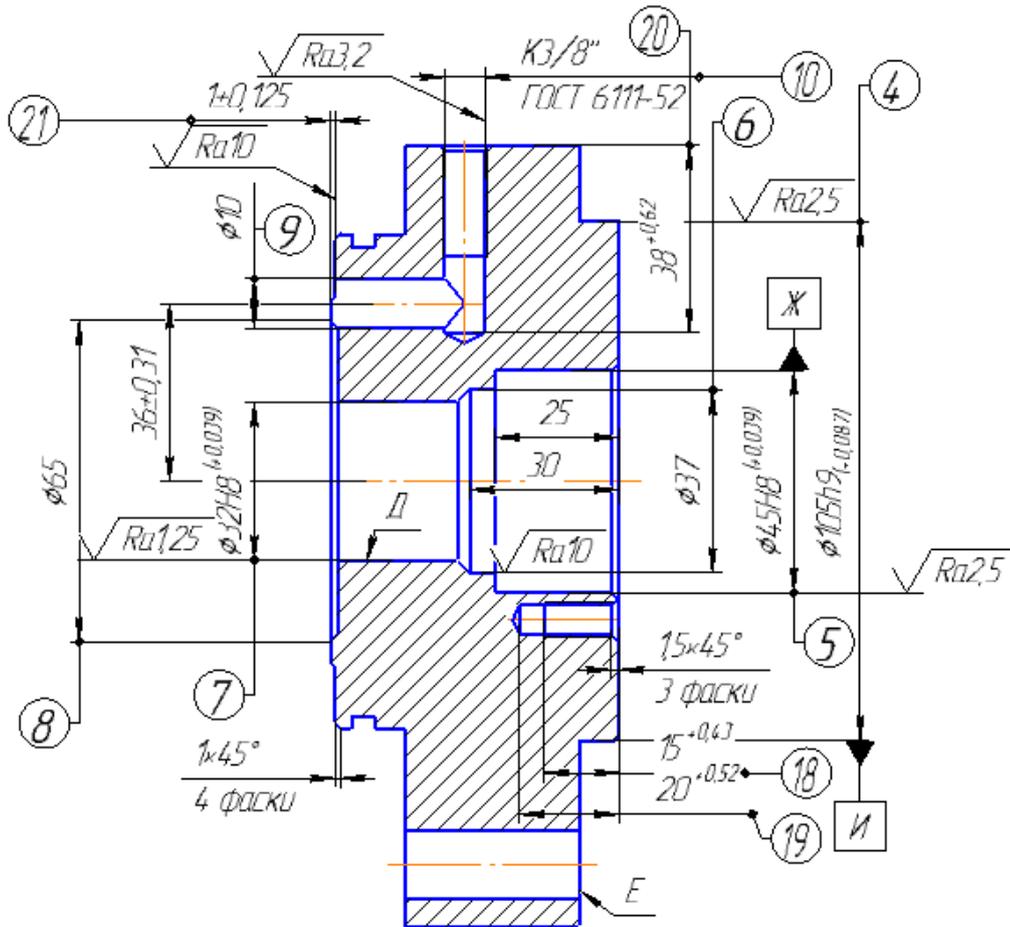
Разрез А–А по чертежу. Нумерование поверхностей детали
